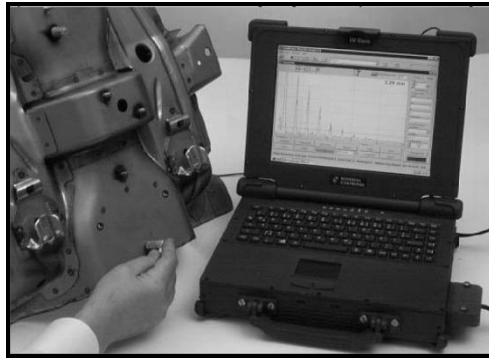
Inspección ultrasónica de soldadura de puntos^[7]
